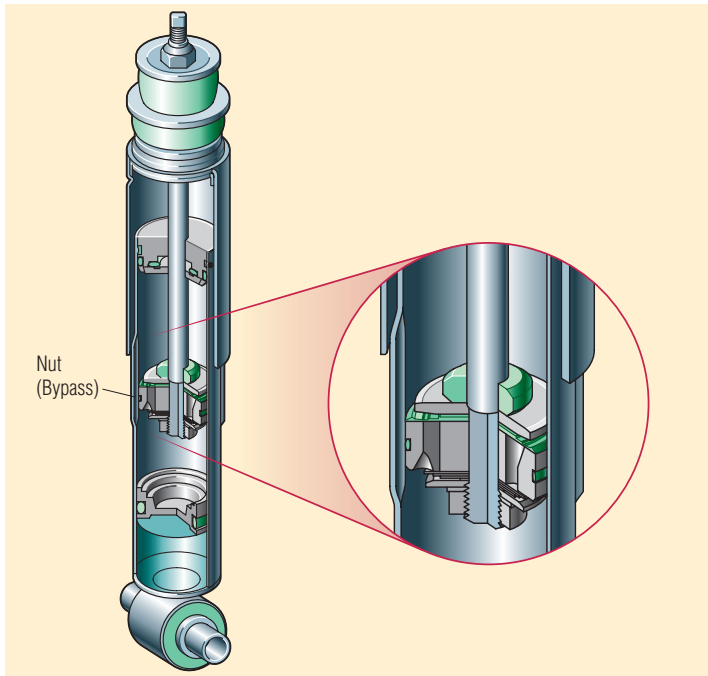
Schwingungsdämpfer mit Bypasstechnik.
